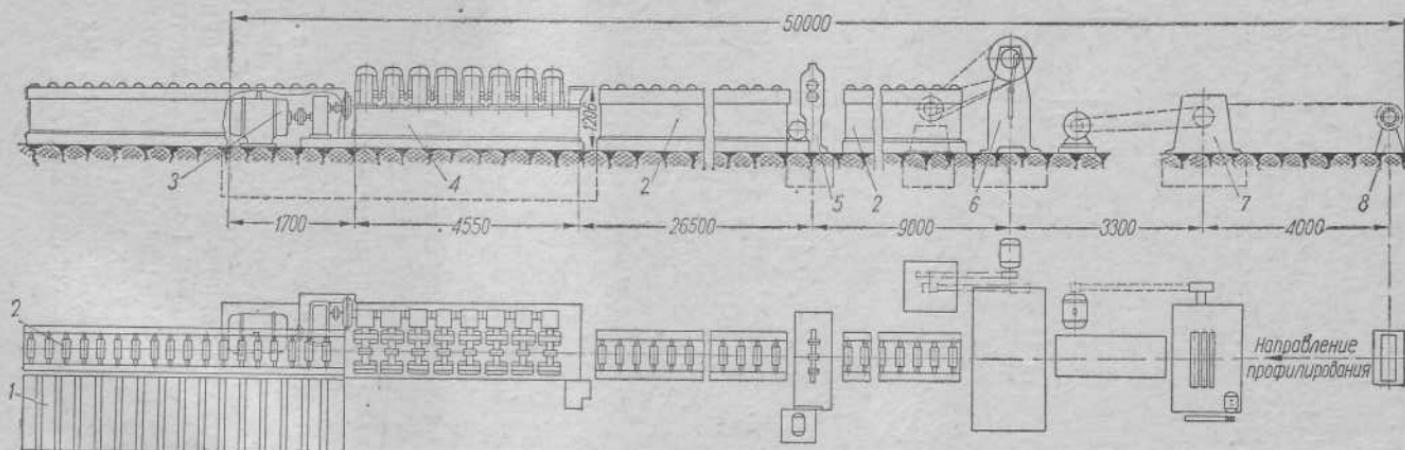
Схема расположения оборудования профилегибочного агрегата периодического действия:
